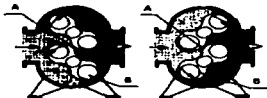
Compresor Root. A) Juego entre rotadores. B) Rotor matriz
